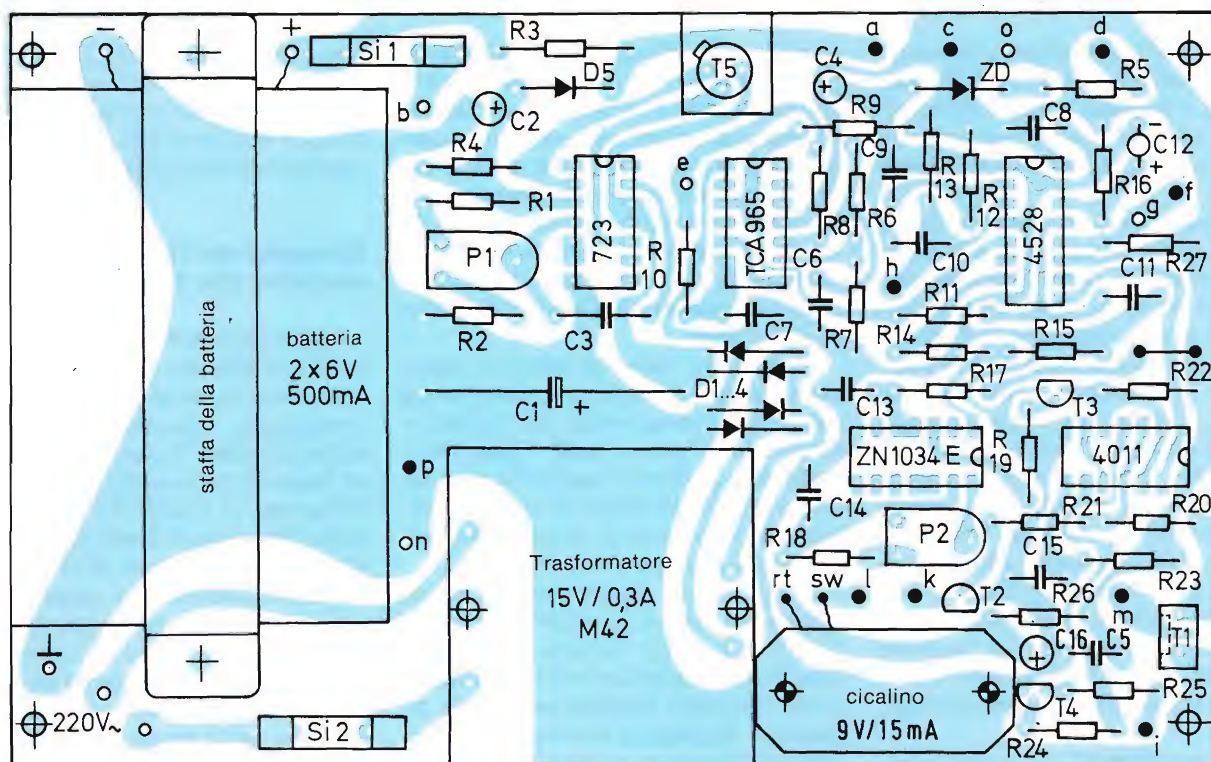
Disposizione dei componenti sul circuito stampato.
